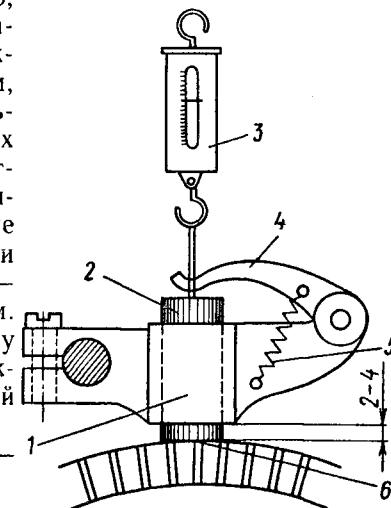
Устройство для измерения динамометром давления щетки на коллектор
